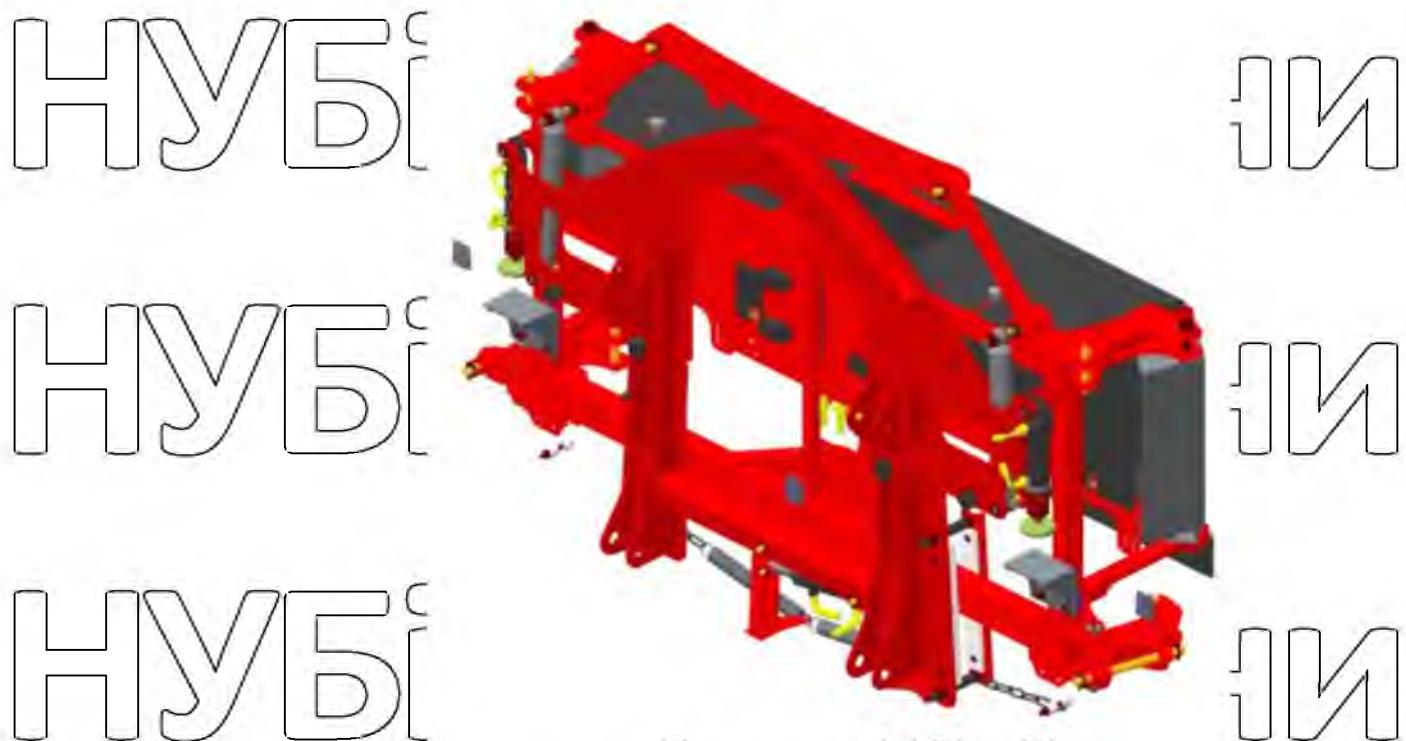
Загальний вигляд підвіски EQUILIBRA
